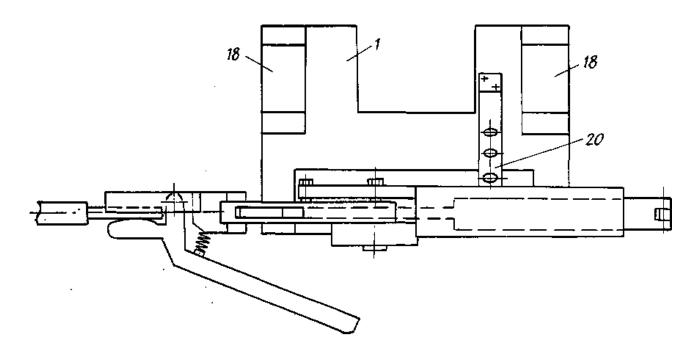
Устройство для сварки наклонным электродом вид сверху
